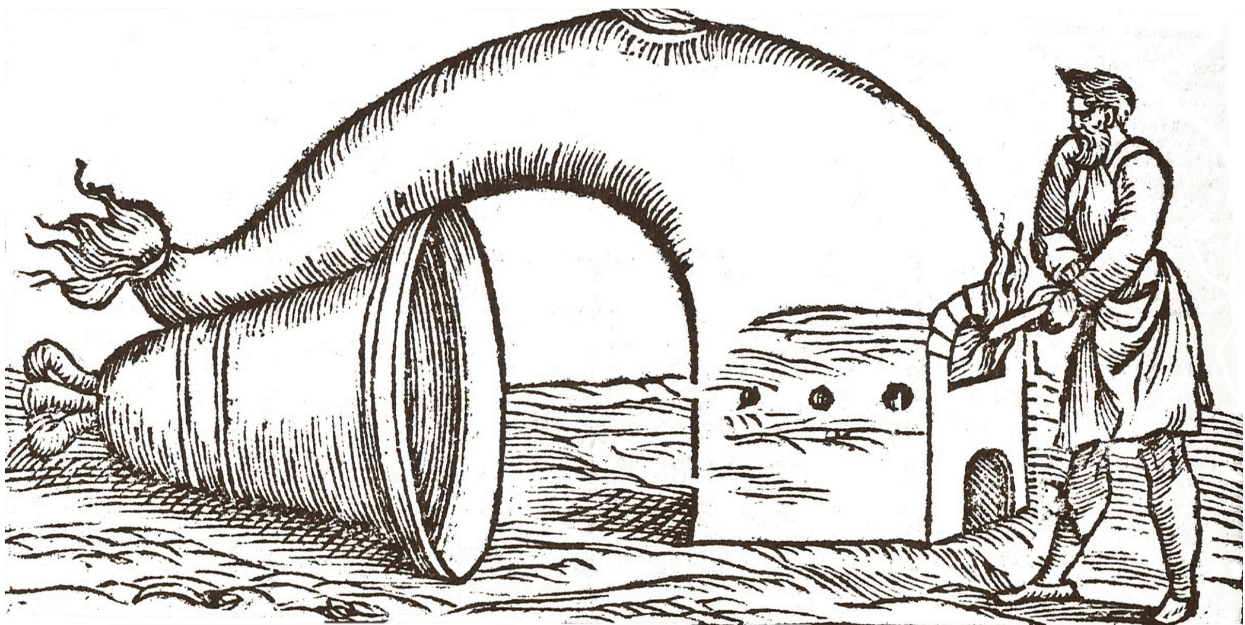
Saldatura della campana fessurata nel disegno tratto dal testo di Biringuccio.
